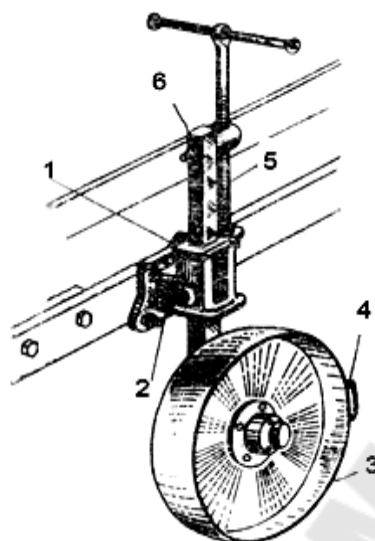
Опорное колесо: 1 – скоба; 2 – детали крепления; 3 – колесо; 4 – чистик; 5 – механизм винтовой; 6 – стойка
